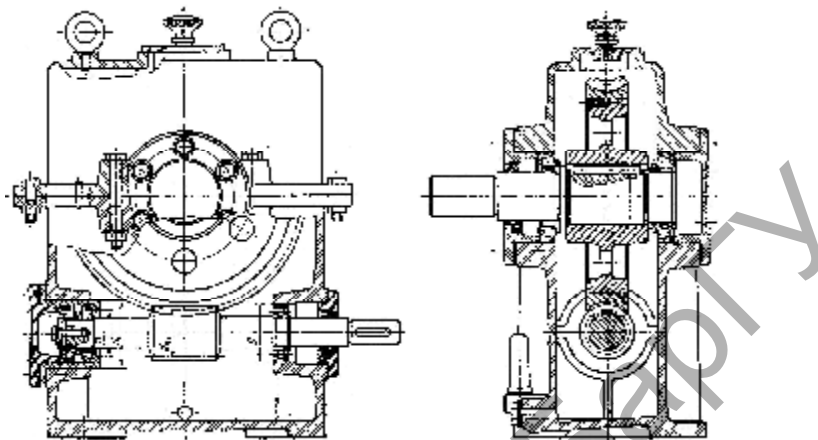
Одноступенчатый редуктор с нижним расположением червяка [18]
